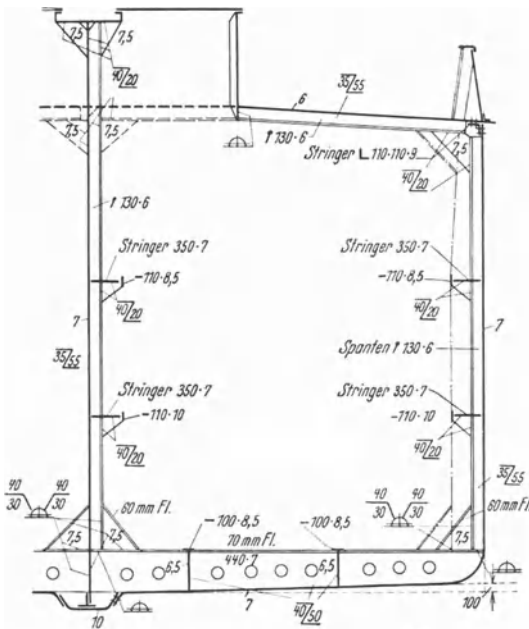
Geschweißter Hauptspant eines Ölfahrzeugs.
